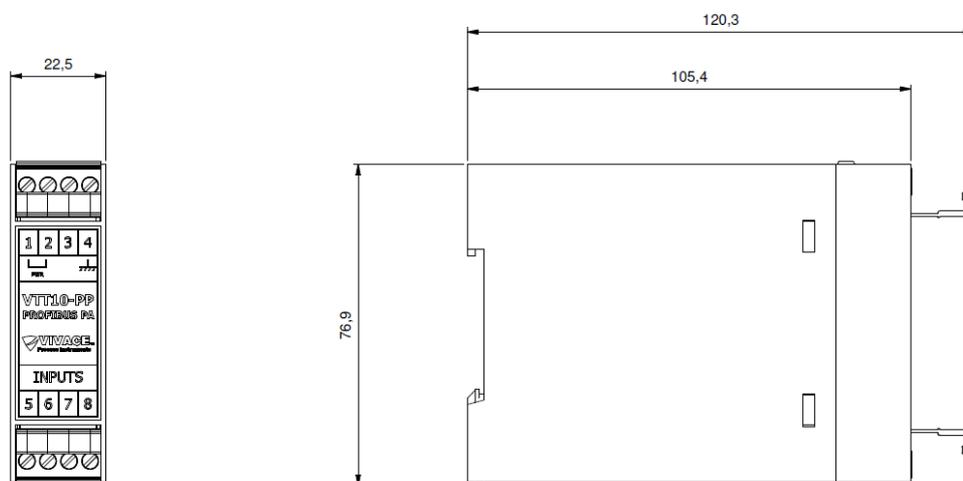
Desenho dimensional e esquema de montagem do VTT10-PP.
